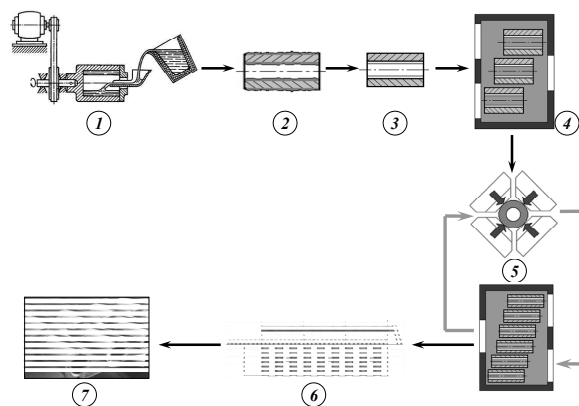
Вариант технологии изготовления оси из центробежнолитой заготовки (многократная ковка)
